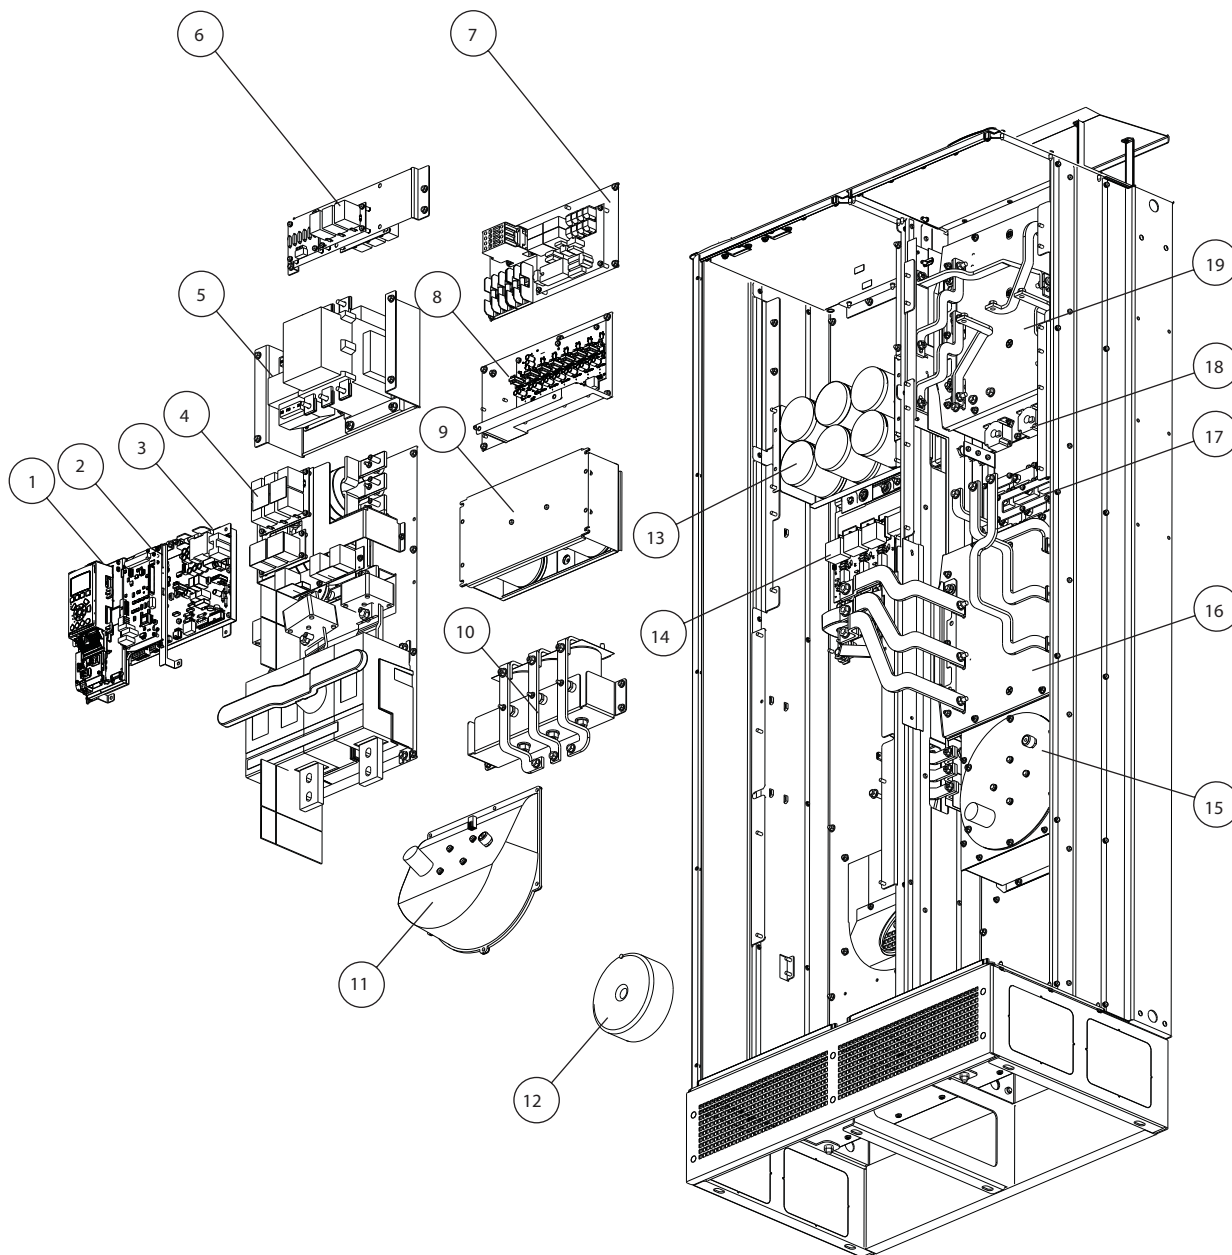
Explosionszeichnung AAF005 Baugröße D
